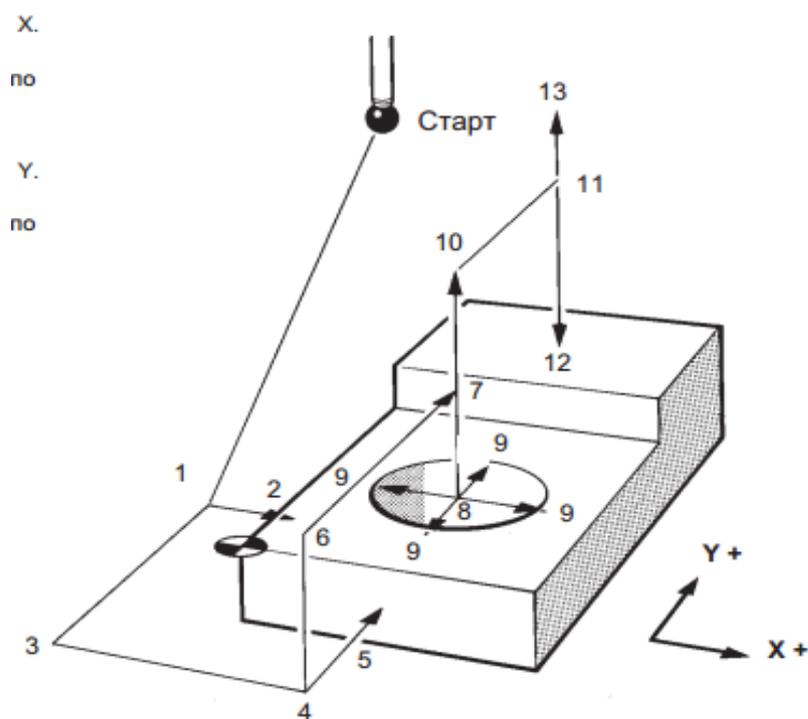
Схема привязки детали датчиком контактного измерения Renishaw
